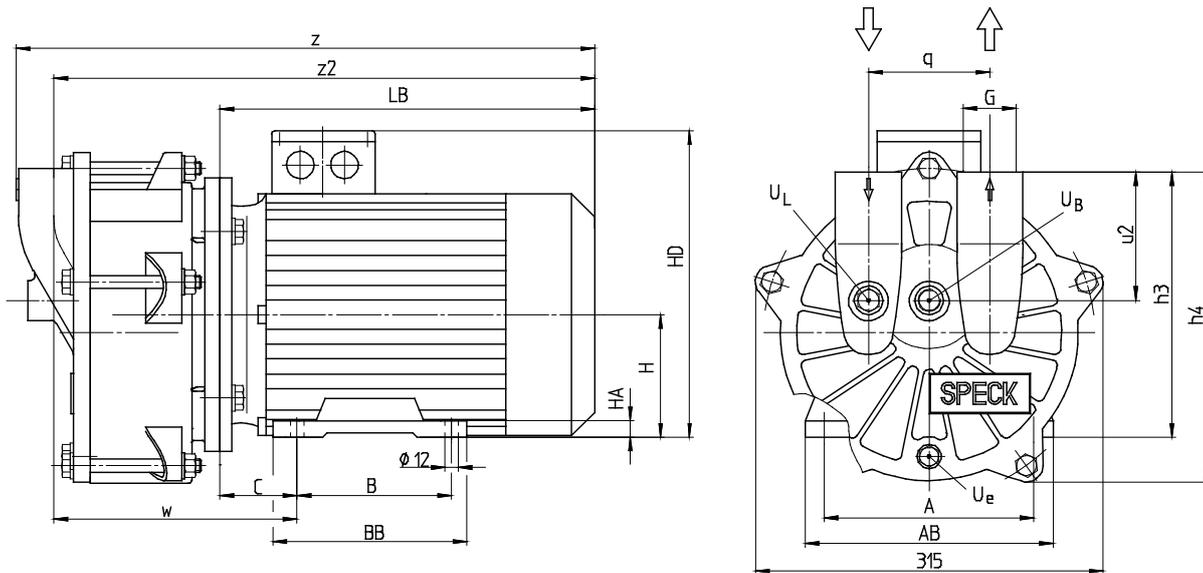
Maßzeichnung VG-95/130/155/255 – Gewindeausführung
